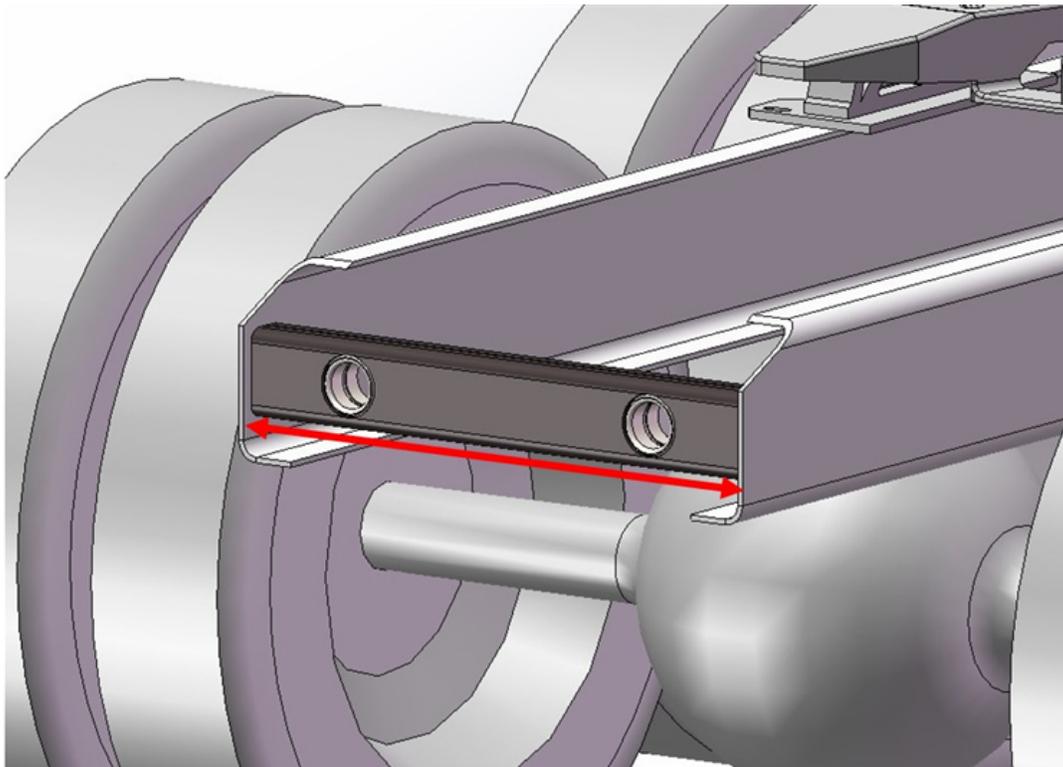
SOUDURE DU RÉCEPTACLE ARRIÈRE (QUICKSWAP AVEC BÉQUILLES OU ESSIEU D'APPOINT)
